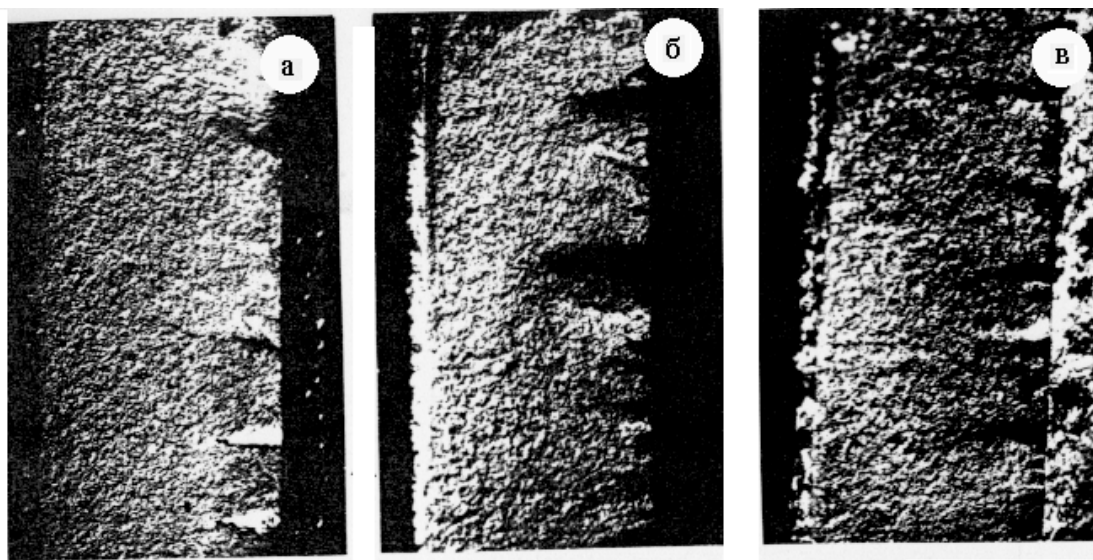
Фото зломів зразків на повітрі: а) без попередньої корозії і покриття; б) з попередньою корозією без покриття; в) з попередньою корозією і покриттям
